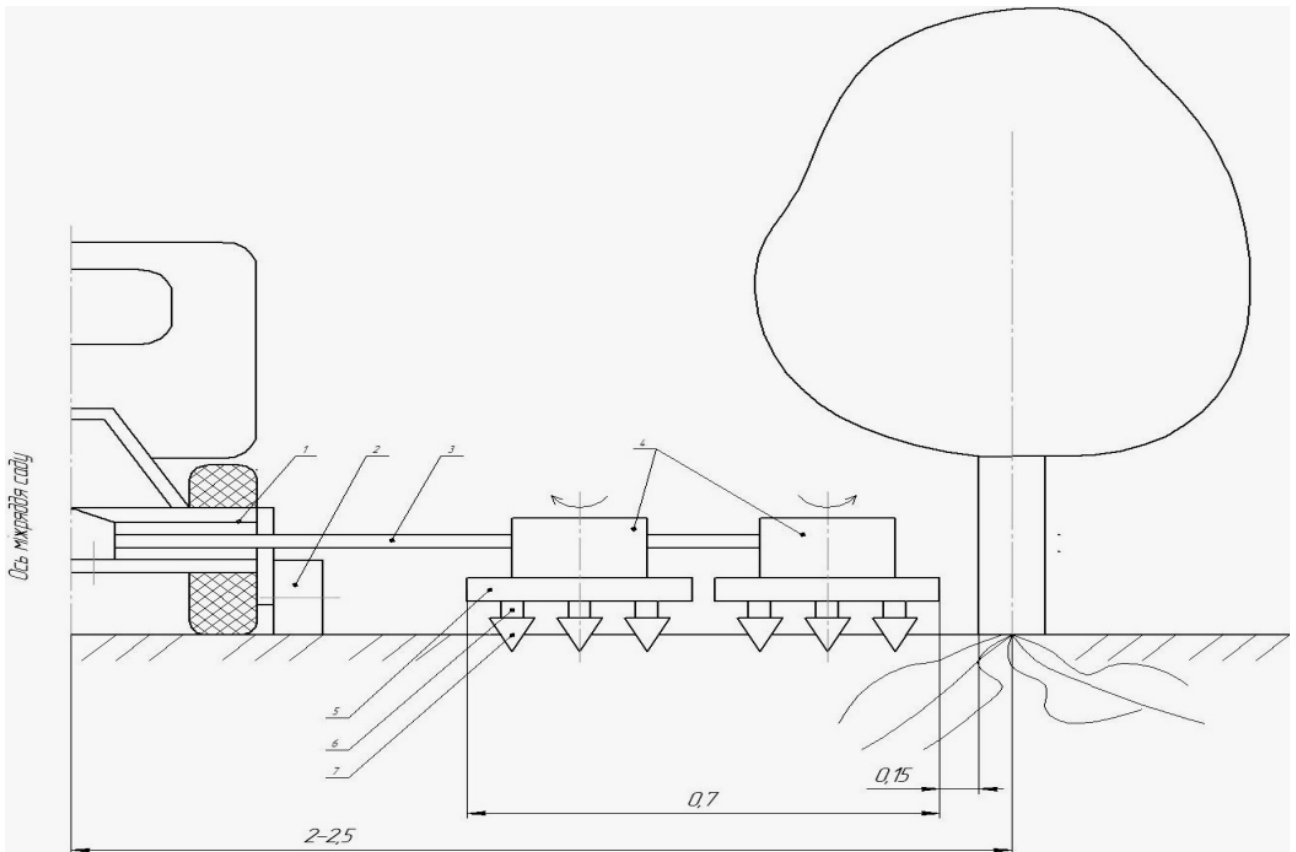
Конструктивно-технологічна схема фрезерної машини:
